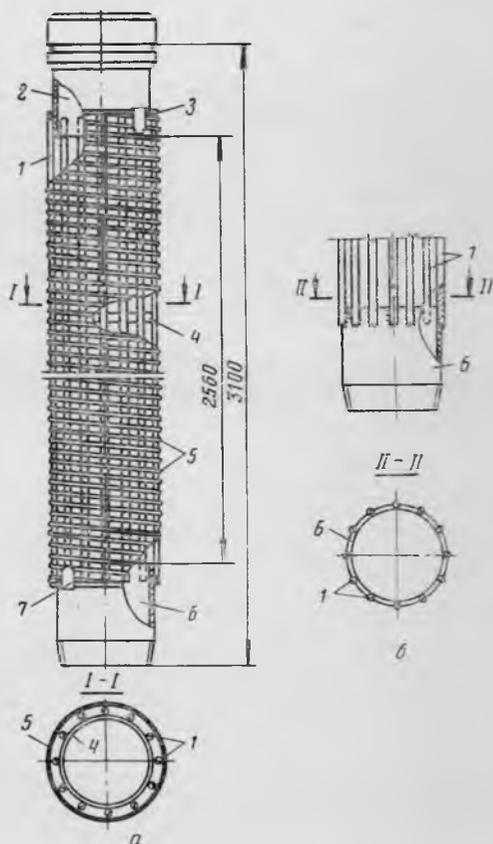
Каркасно-стержневой фильтр с проволочной обмоткой: а — общий вид; б — соединение патрубка со стержнями «впотаи»; 1 — металлические стержни; 2 — соединительный патрубок с полумуфтой; 3 — торцевое кольцо; 4 — опорный пояс; 5 — обмоточная проволока; 6 — соединительный патрубок с резьбой; 7 — прижимная планка.
